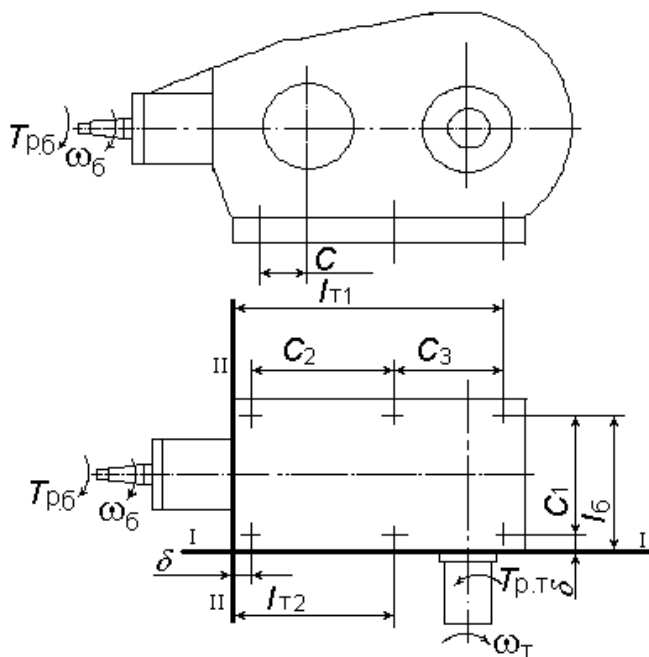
Схема нагружения болтов крепления редуктора к раме
